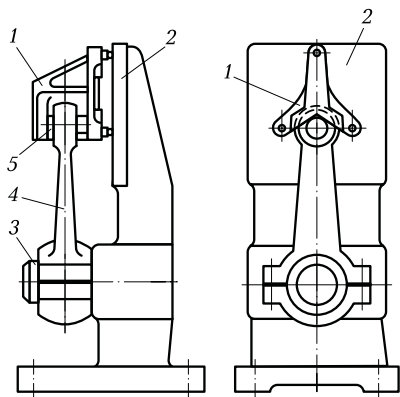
Приспособление для контроля параллельности осей отверстий шатуна:
